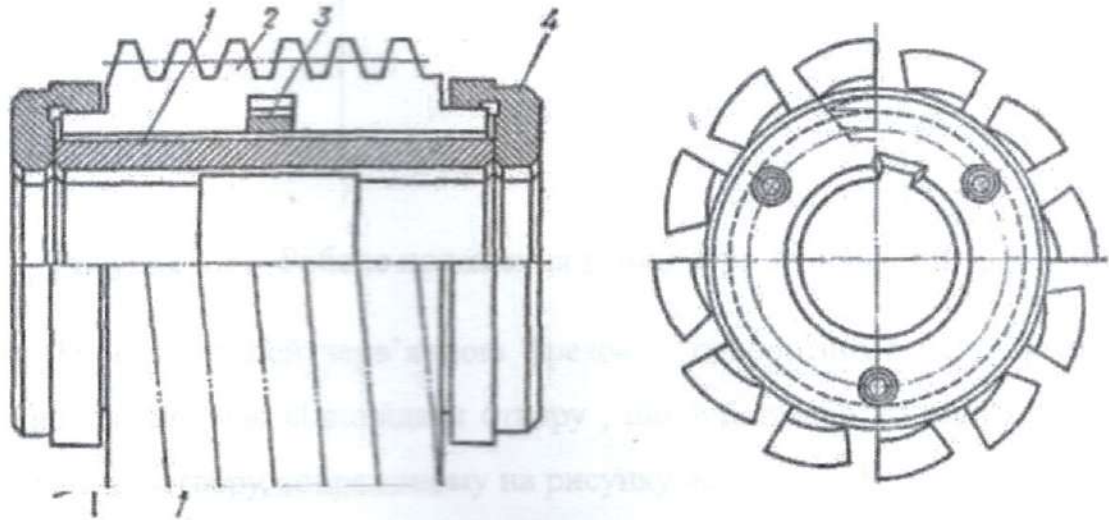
Збірна черв'ячна фреза з поворотними рейками ВНДІ
